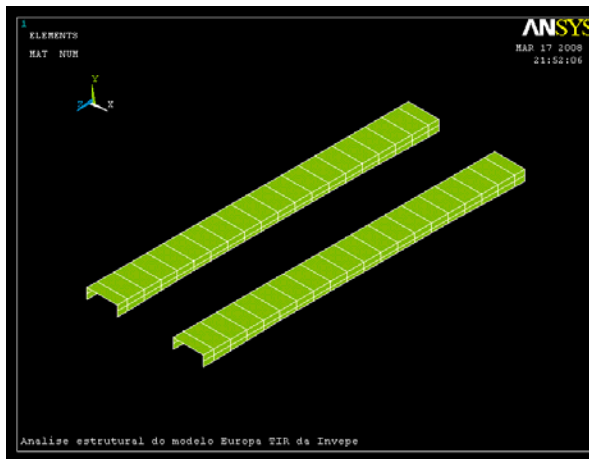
Travessa de Perfil em U da Placa do KP (análise 9)
